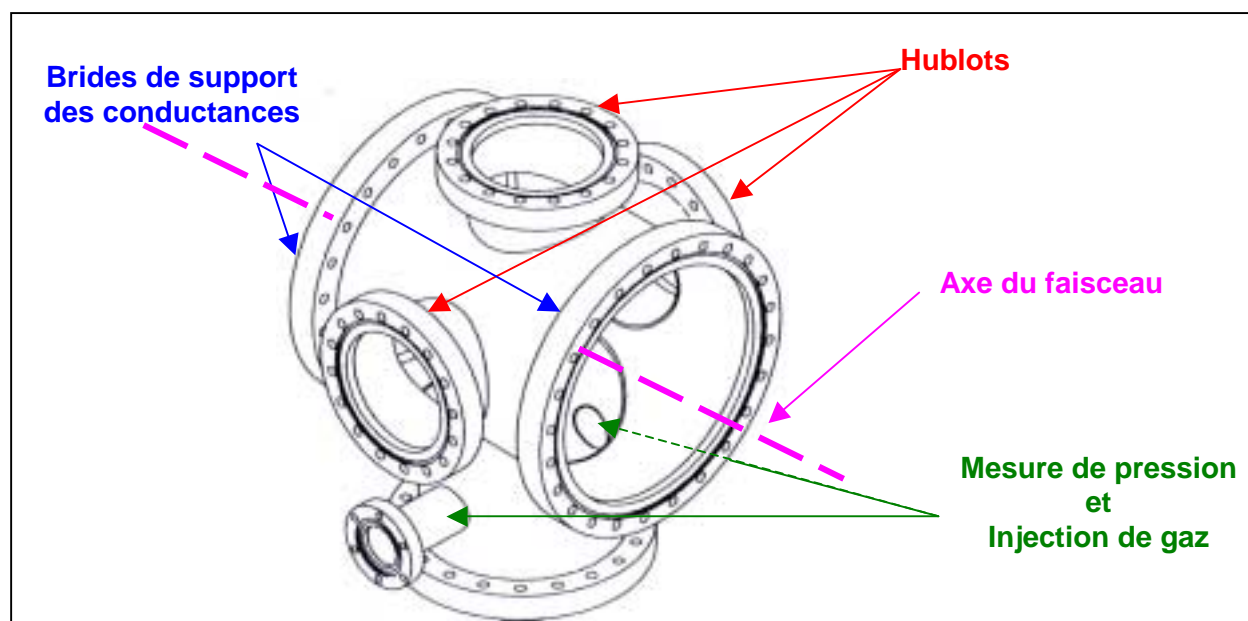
Dessin de la chambre d'injection gazeuse.
